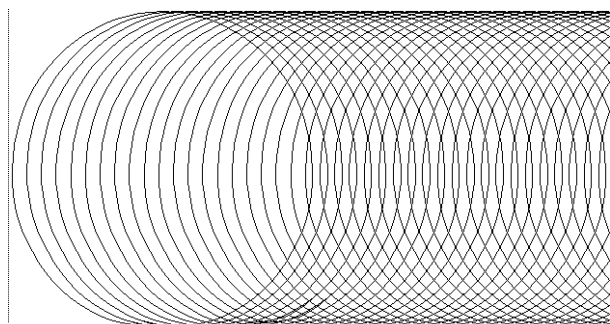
Схема траектории движения зубьев фрезы при торцевом фрезеровании.
